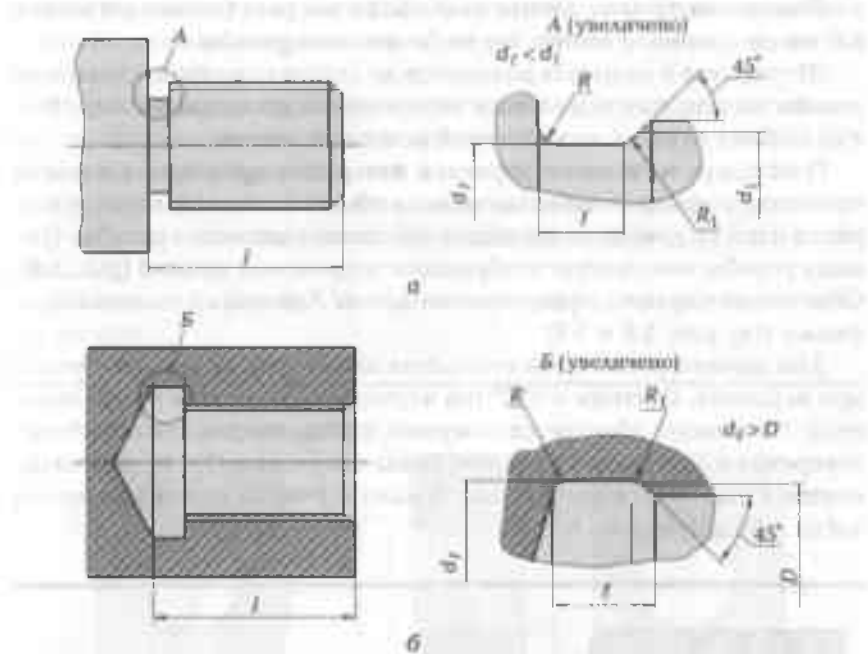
Технологические элементы наружной [а] и внутренней [б] резьбы: d_c — диаметр проточки; R — радиус сопряжения с телом обрабатываемой детали; l — радиус скругления при выходе инструмента после нарезания резьбы; R_1 — радиус, получаемый при нарезании резьбы на обрабатываемой детали технологическим инструментом; остальные обозначения см. на рис. 5.1 и 5.6
